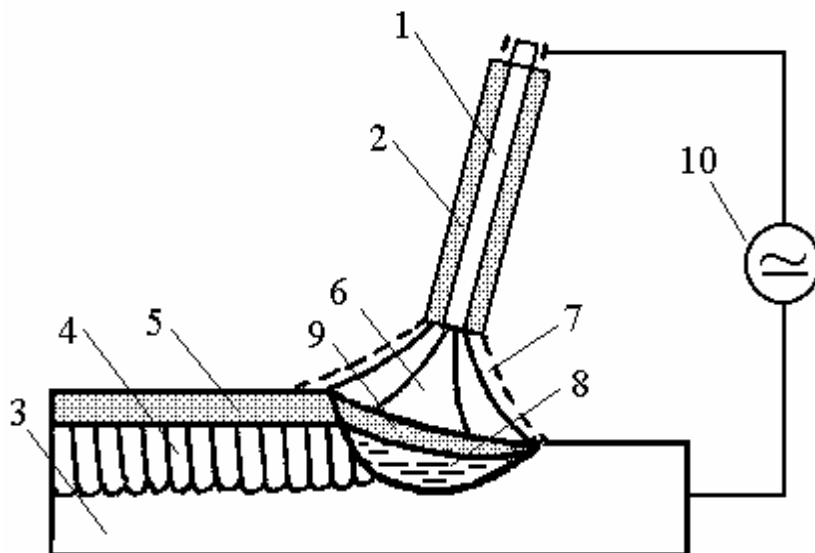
Схема ручной дуговой сварки плавящимся электродом с покрытием:
